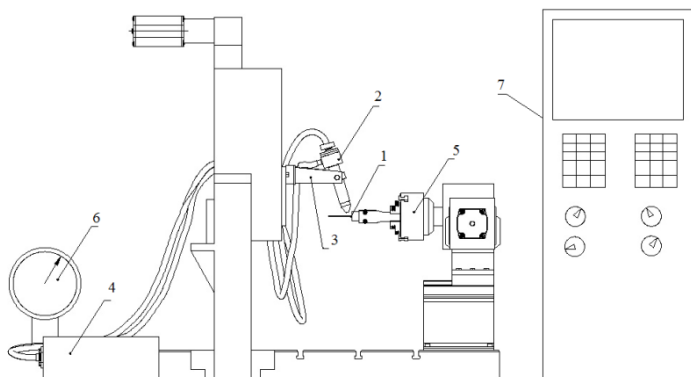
Экспериментальная установка для нанесения покрытия: 1 — образец; 2 — сопло; 3 — крепежная стойка; 4 — блок питания; 5 — шпиндель для закрепления образца; 6 — манометр; 7 — система управления оснащена ЧПУ
